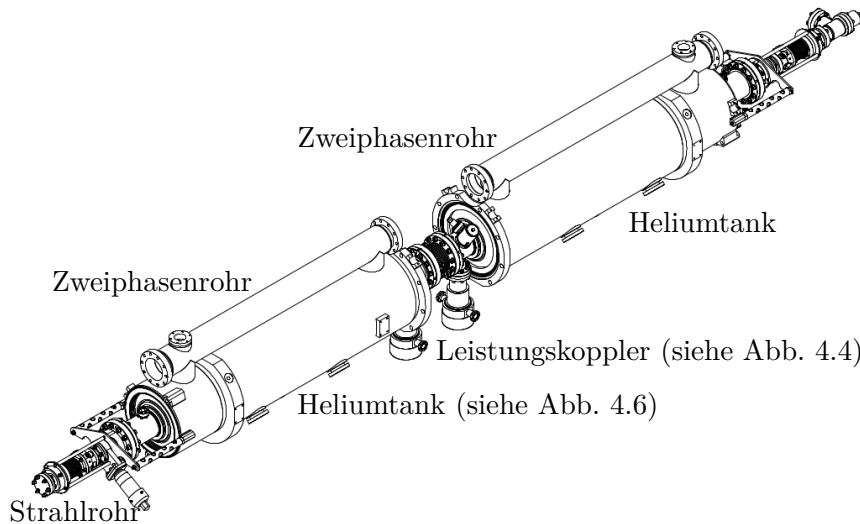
Der Coldstring des Kryomoduls umfasst die beiden TESLA-Kavitäten in ihren Heliumtanks und die umliegenden Anbaugruppen. Die Gesamtlänge des Coldstrings bei MESA beträgt 3,3 m. Die Zeichnung ist [52] entnommen.
